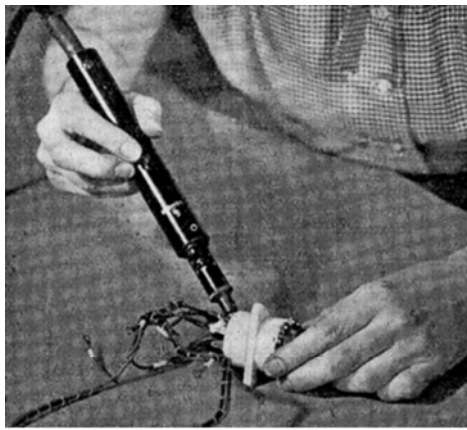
Anschweißen von Leitungen an eine Röhrenfassung mit dem Schweißgriffel.
